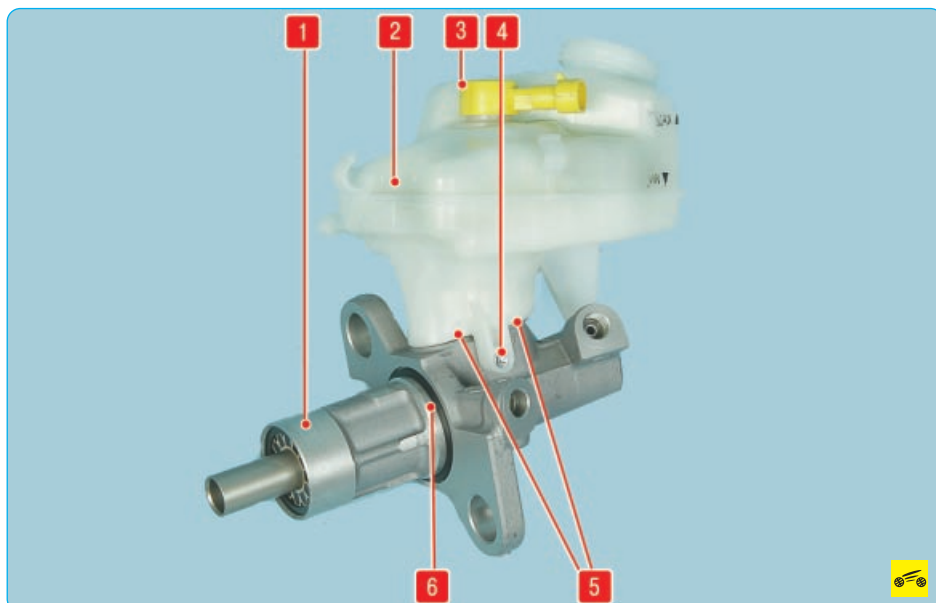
Главный тормозной цилиндр с бачком: 1 — главный тормозной цилиндр; 2 — бачок главного тормозного цилиндра; 3 — датчик уровня тормозной жидкости; 4 — винт крепления бачка; 5 — соединительные втулки; 6 — уплотнительное кольцо фланца главного тормозного цилиндра
